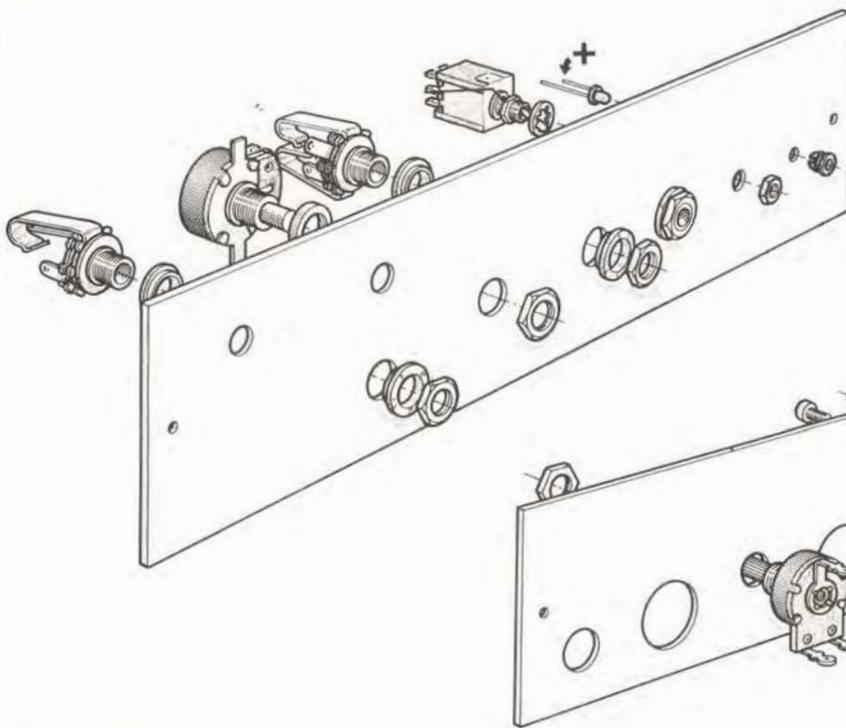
Fissaggio dei comandi sul pannello frontale.
